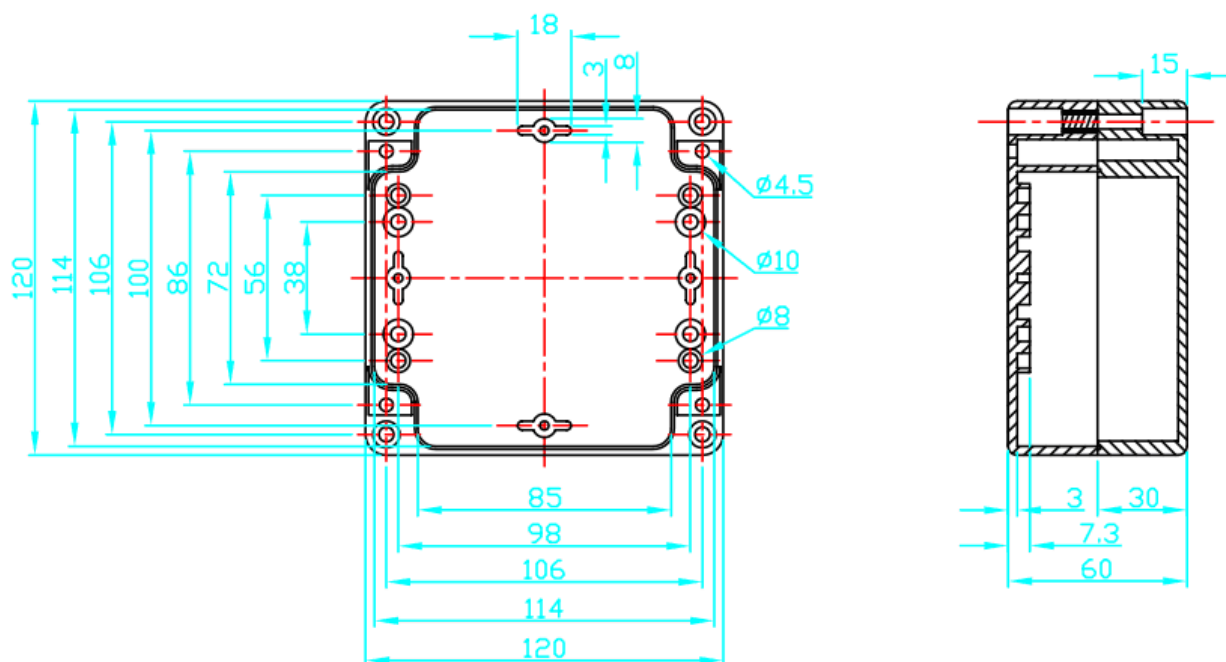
Схема корпуса G386/278 фирмы Gainta с указанием размеров
